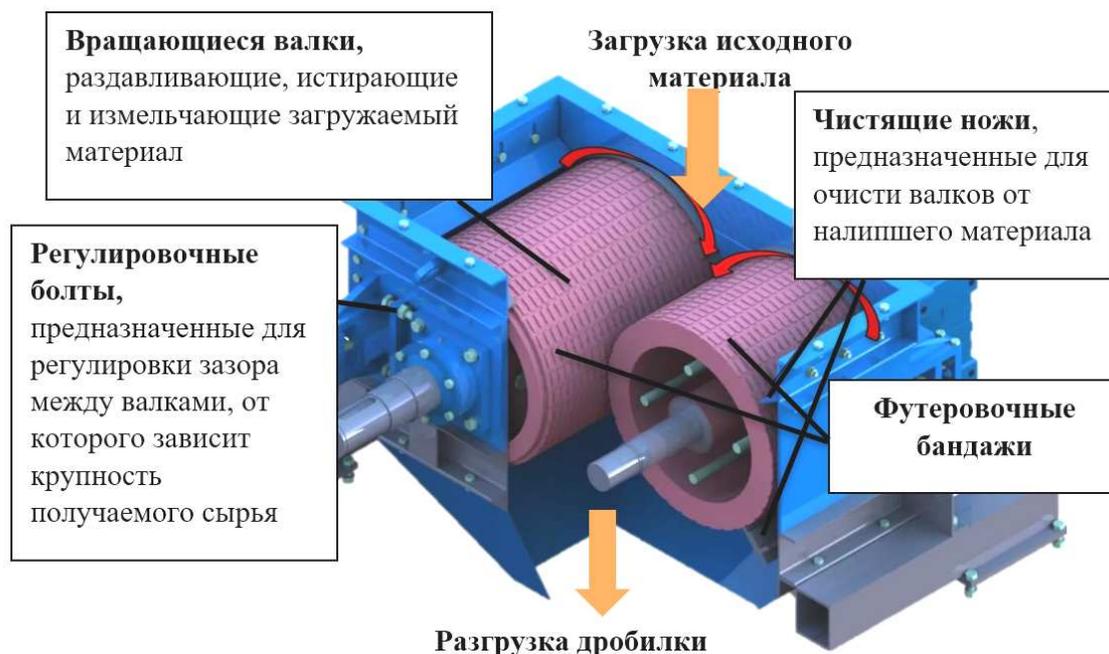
Принцип работы и устройство валковой дробилки (составлено авторами)
